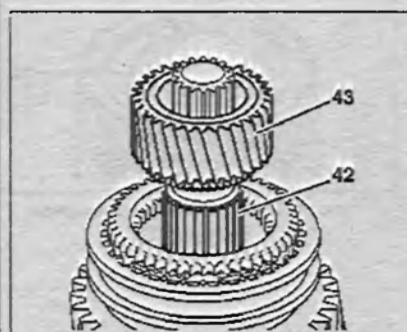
Снимите шестерню 43 5-й передачи и игольчатый подшипник 42.
